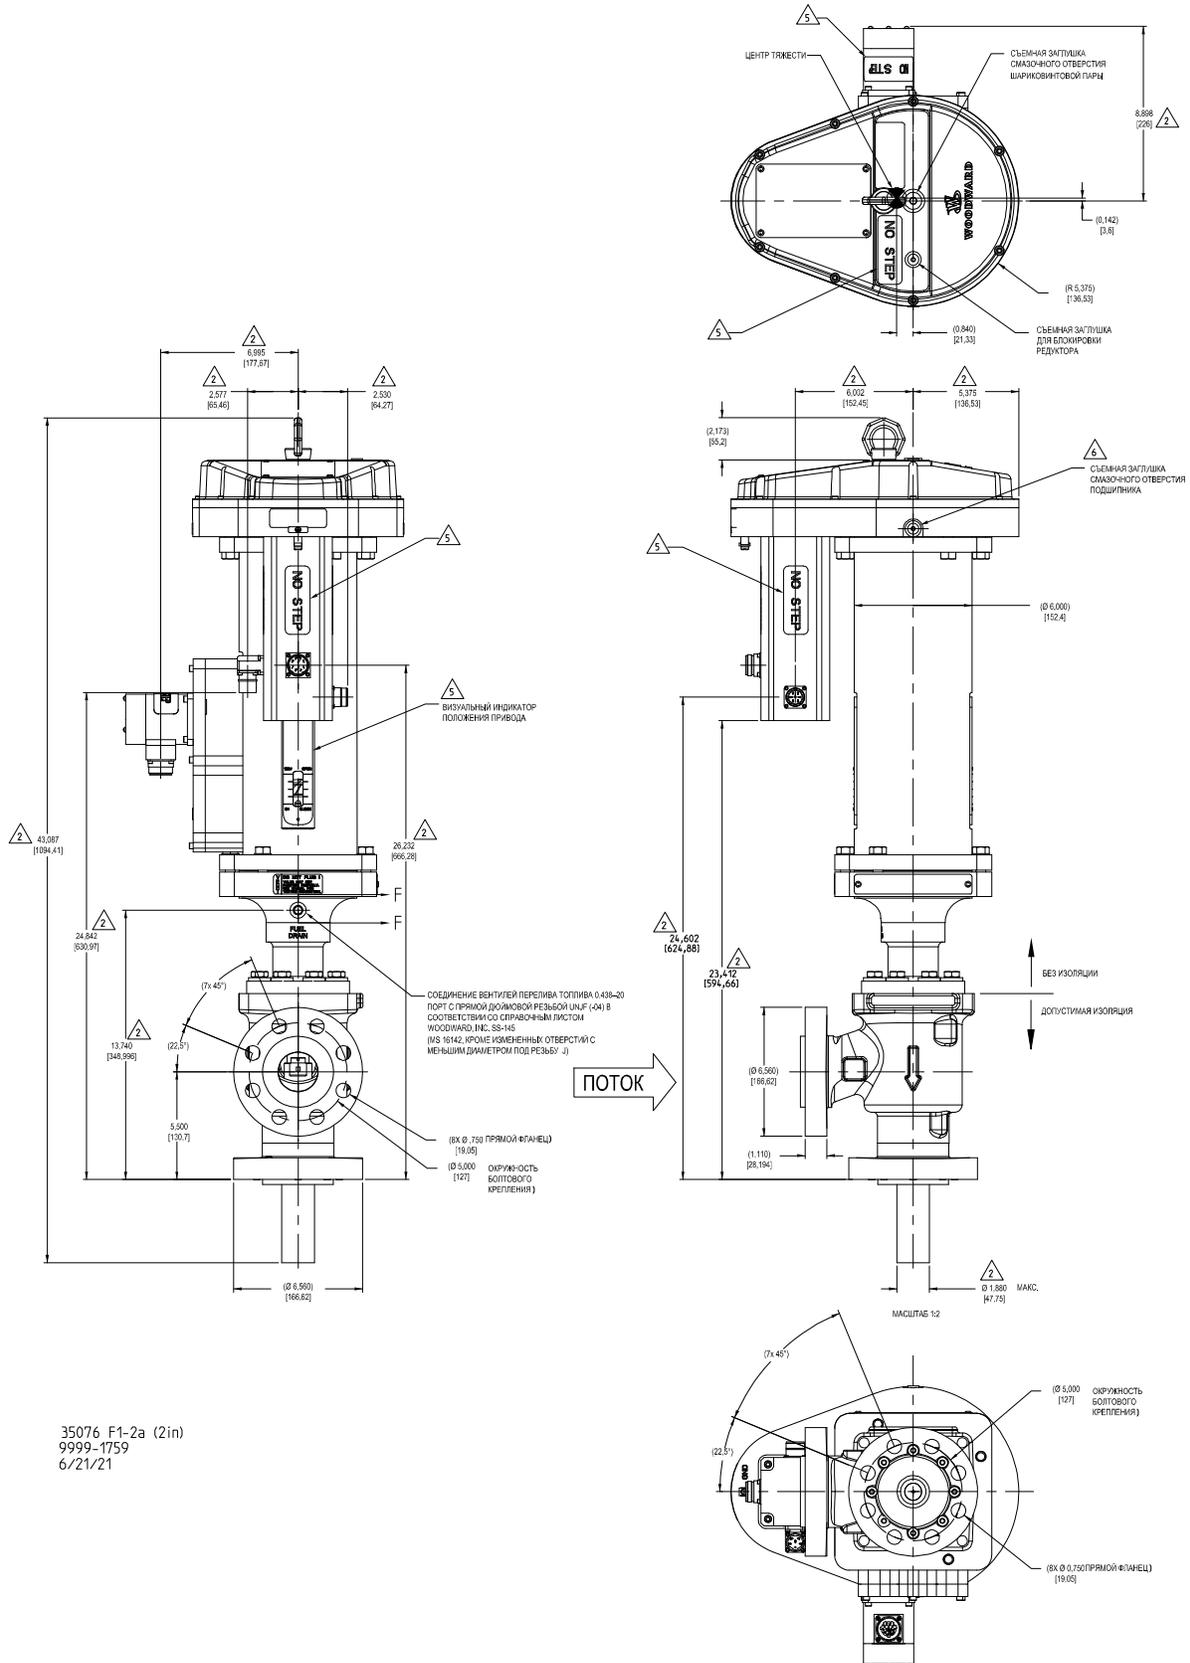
а. Габаритный чертеж (2-дюймовый клапан LESV II со сверхвысоким коэффициентом восстановления, нержавеющая сталь, двойной резервер класса 600#)
